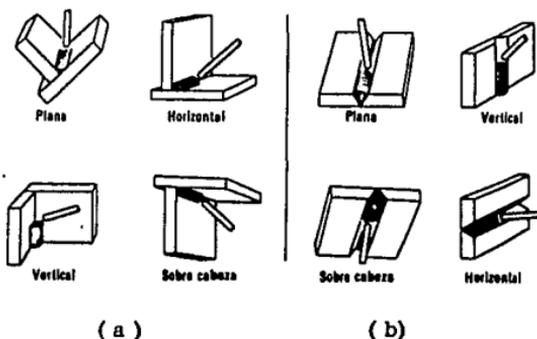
Posiciones para soldar: (a) Soldaduras de Filete, (b) Soldaduras a tope.
